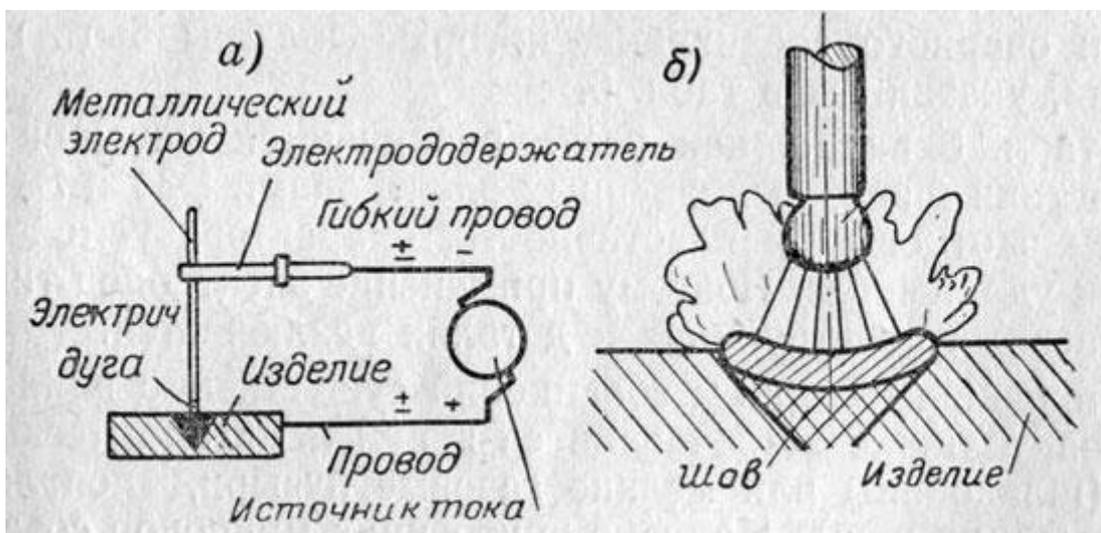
Ручная дуговая сварка покрытым электродом
